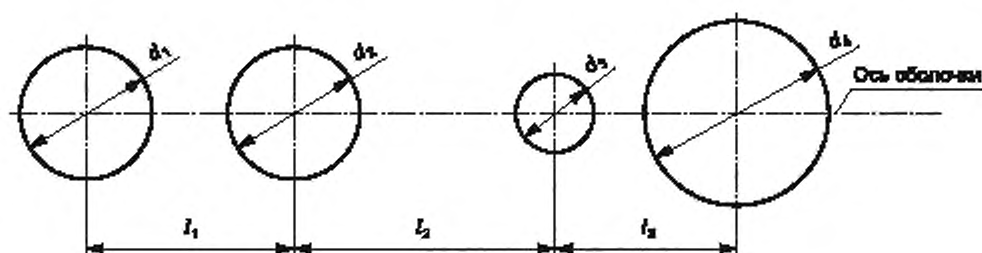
Ряд отверстий с неодинаковыми отверстиями и шагами
